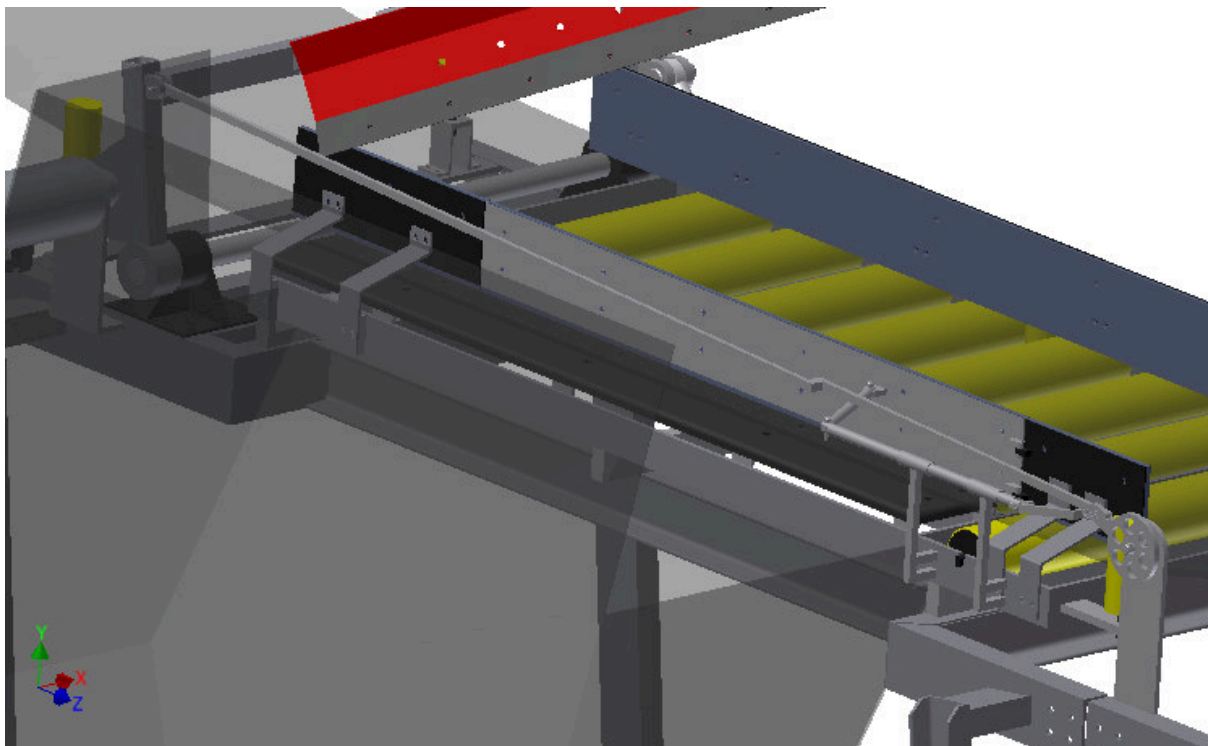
Schéma polohy mechanismu při otevřené bočnici na straně výsypky – pohled z boku
